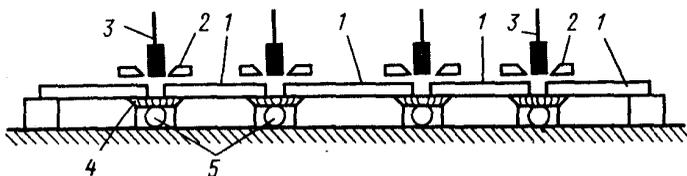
Схема стенда для автоматической сварки листов обечайки
